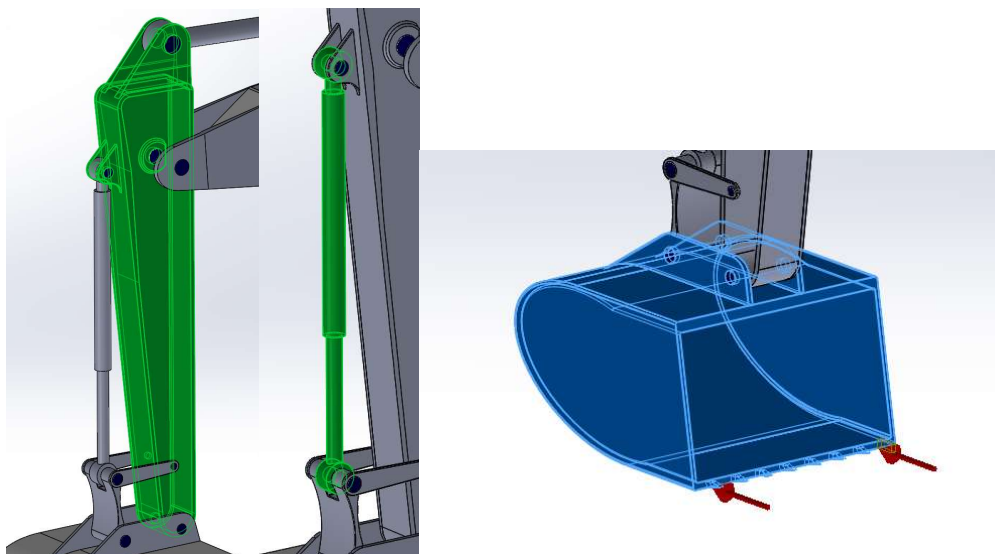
Ensamblajes unidos rígidamente (I)
